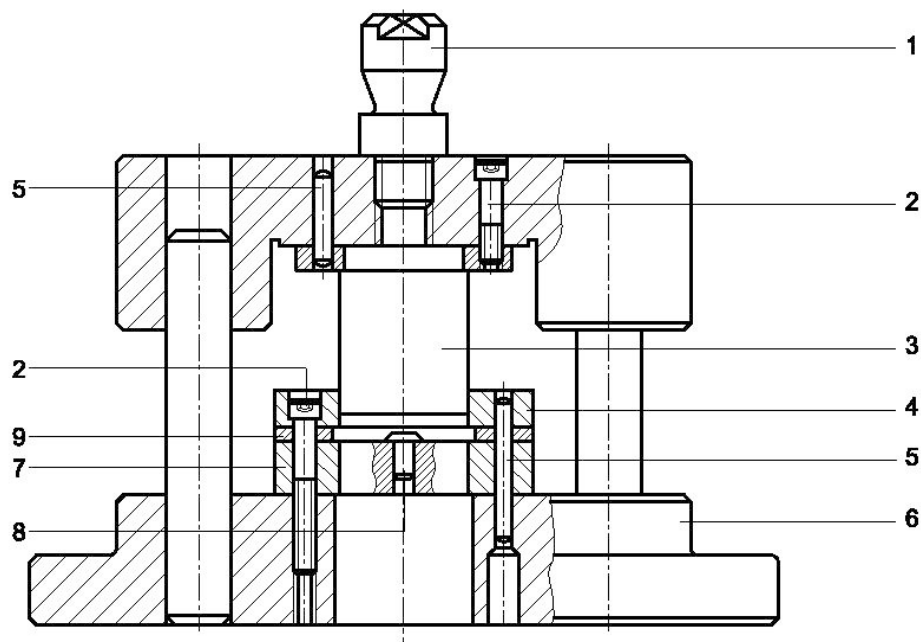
Ausschneidewerkzeug – Säulenführung
